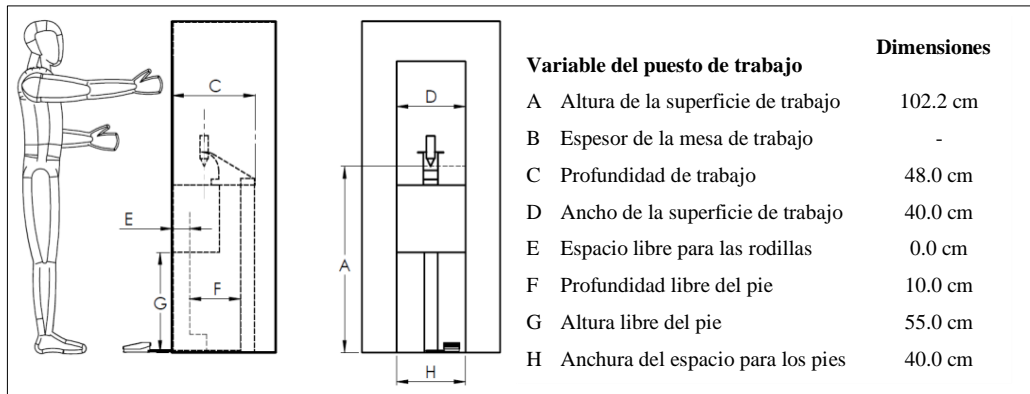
Dimensiones actuales del puesto de colocado de látex en el corte
